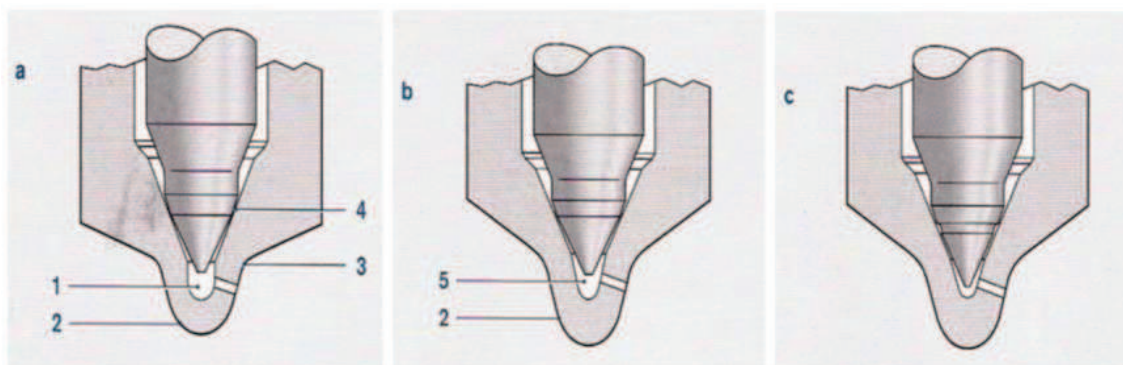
Dimenze vstříkovací techniky pro vznětové motory [1]
